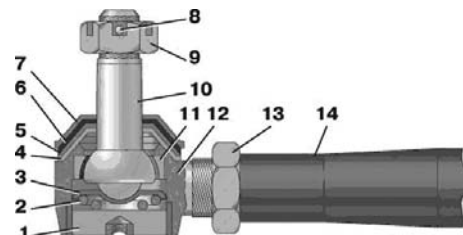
Шарнір рульових тяг: 1 – заглушка; 2 – пружина; 3 – п'ята; 4 – шайба сферична нижня; 5 – шайба сферична верхня; 6 – захисне кільце; 7 – пружинний ковпак; 8 – шплінт; 9, 13 – гайки; 10 – шаровий палець; 11 – сухар; 12 – наконечник; 14 – тяга
